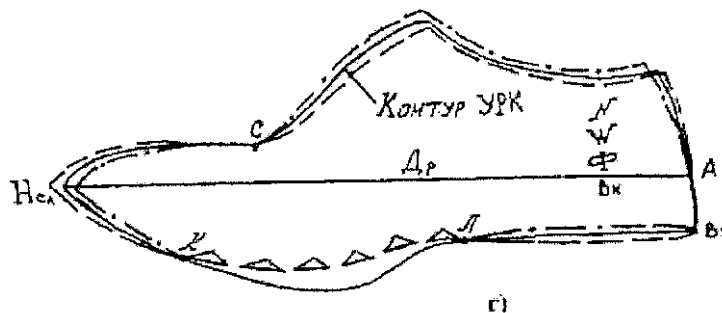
Усереднення розгортки бокової поверхні колодки (УРК)
